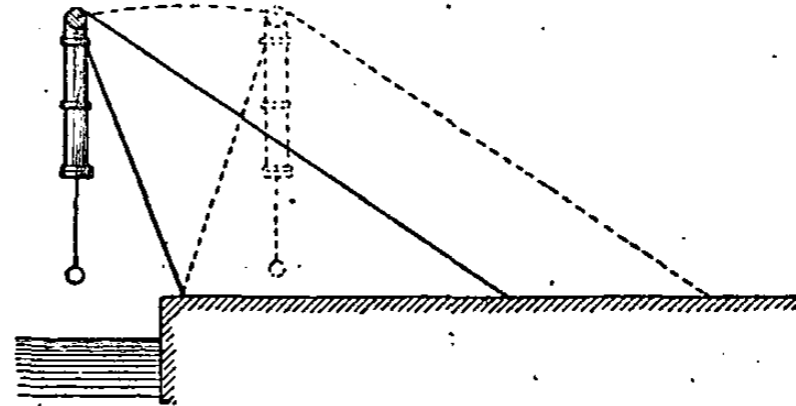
Appareil de levage de la fonderie d'Elswick.
